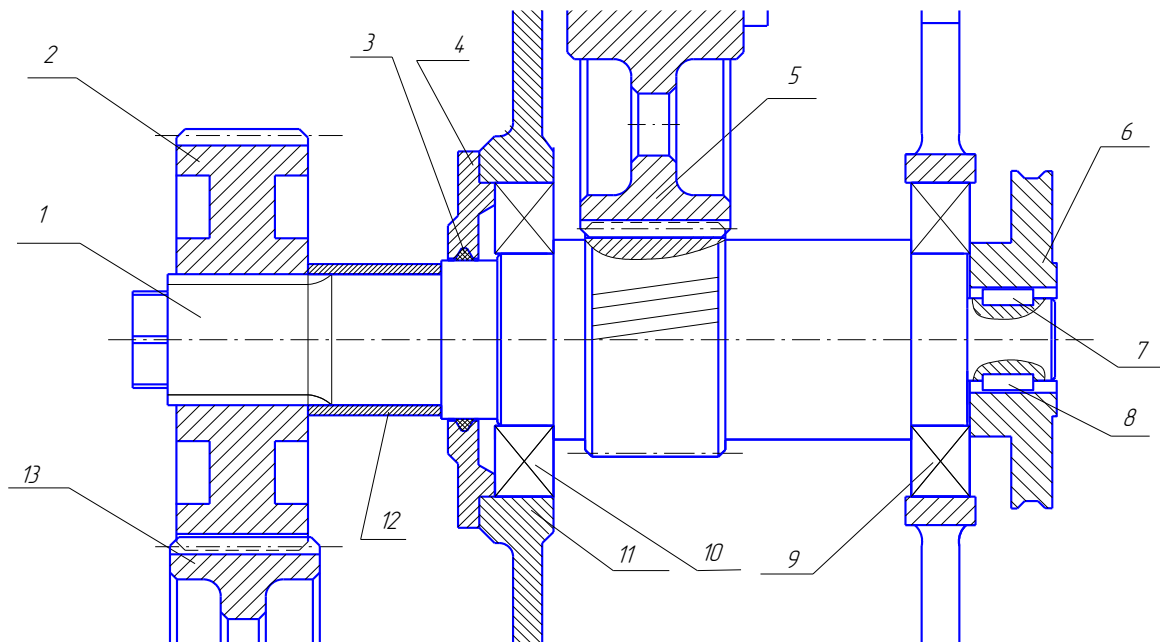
Ескіз вузла редуктора 1ц2у-200
